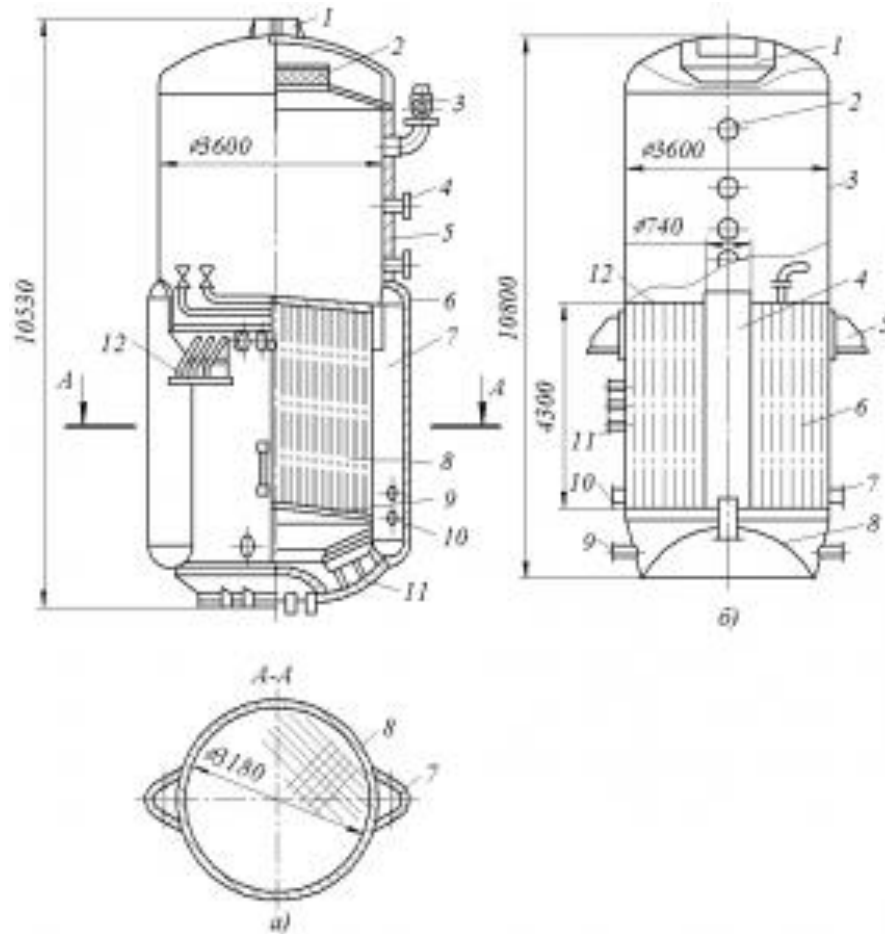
Випарний апарат типу ВЦ: а - з виносними циркуляційними трубами; б - з внутрішньої трубою, корпус 3, в нижній частині якого розташована гріє камера 6 з центральною трубою 4.
